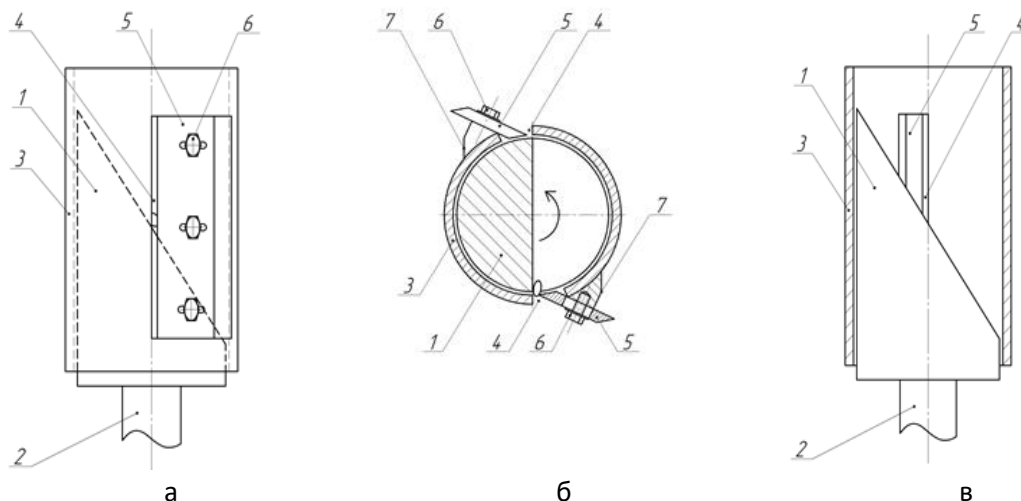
Схема стержневого измельчителя: (а) – главный вид стержневого измельчителя; (б) – поперечный разрез стержневого измельчителя; (в) – продольный разрез стержневого измельчителя; 1 – усеченный стержень; 2 – вал; 3 – цилиндр; 4 – отверстия; 5 – ножи-противорезы; 6 – болты крепления ножей; 7 – подставки ножей
